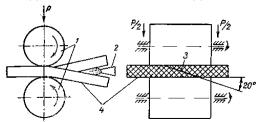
Схема сварки нагретым газом без присадочного материала: 1 – ролики; 2 – нагреватель; 3 –шов; 4 – свариваемые листы.
